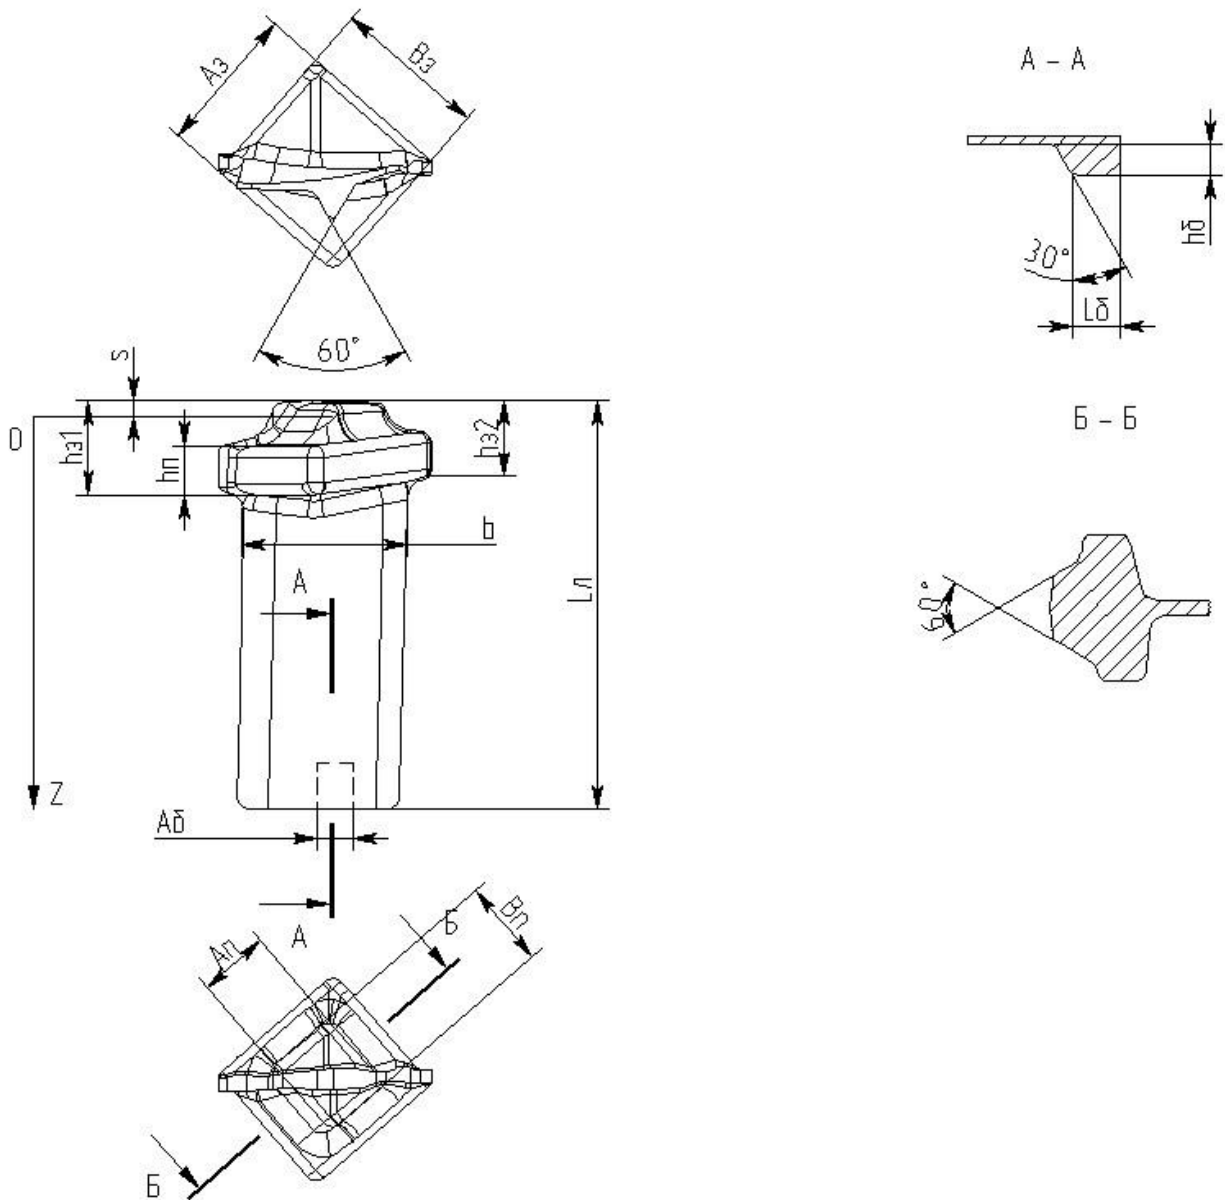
Эскиз поковки лопатки с основными размерами
